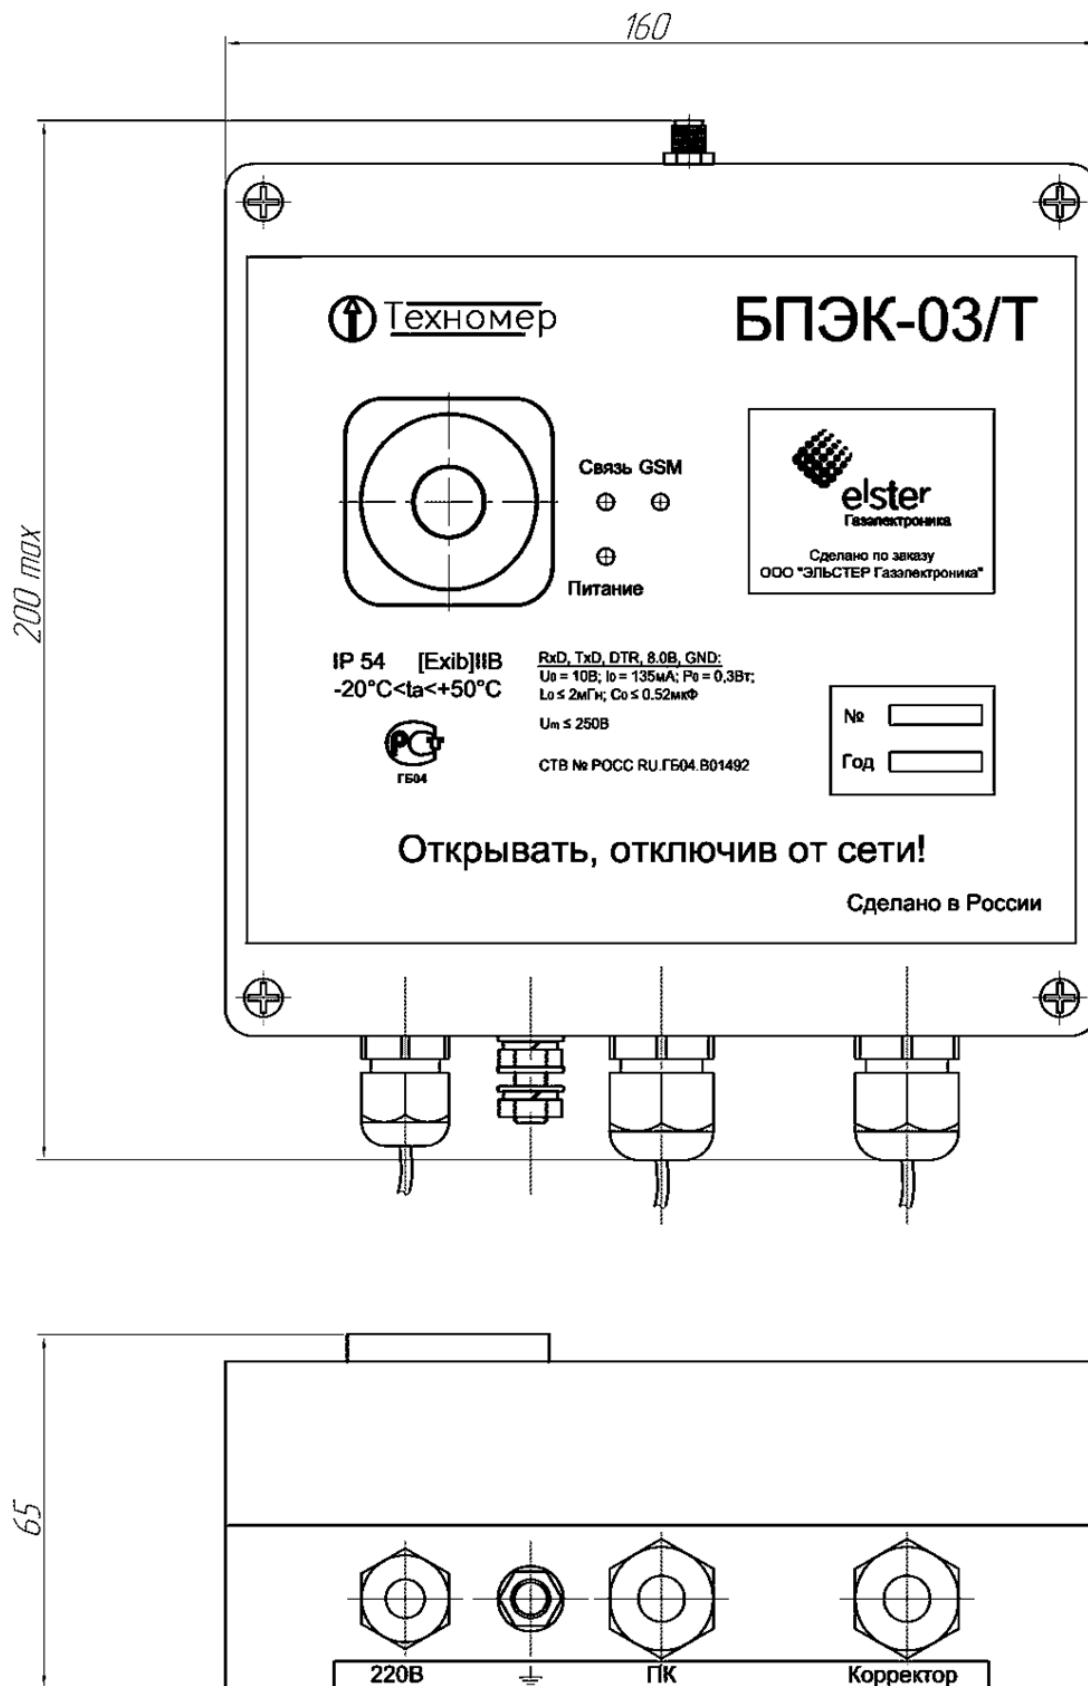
Габаритные размеры блока питания БПЭК-03/Т
